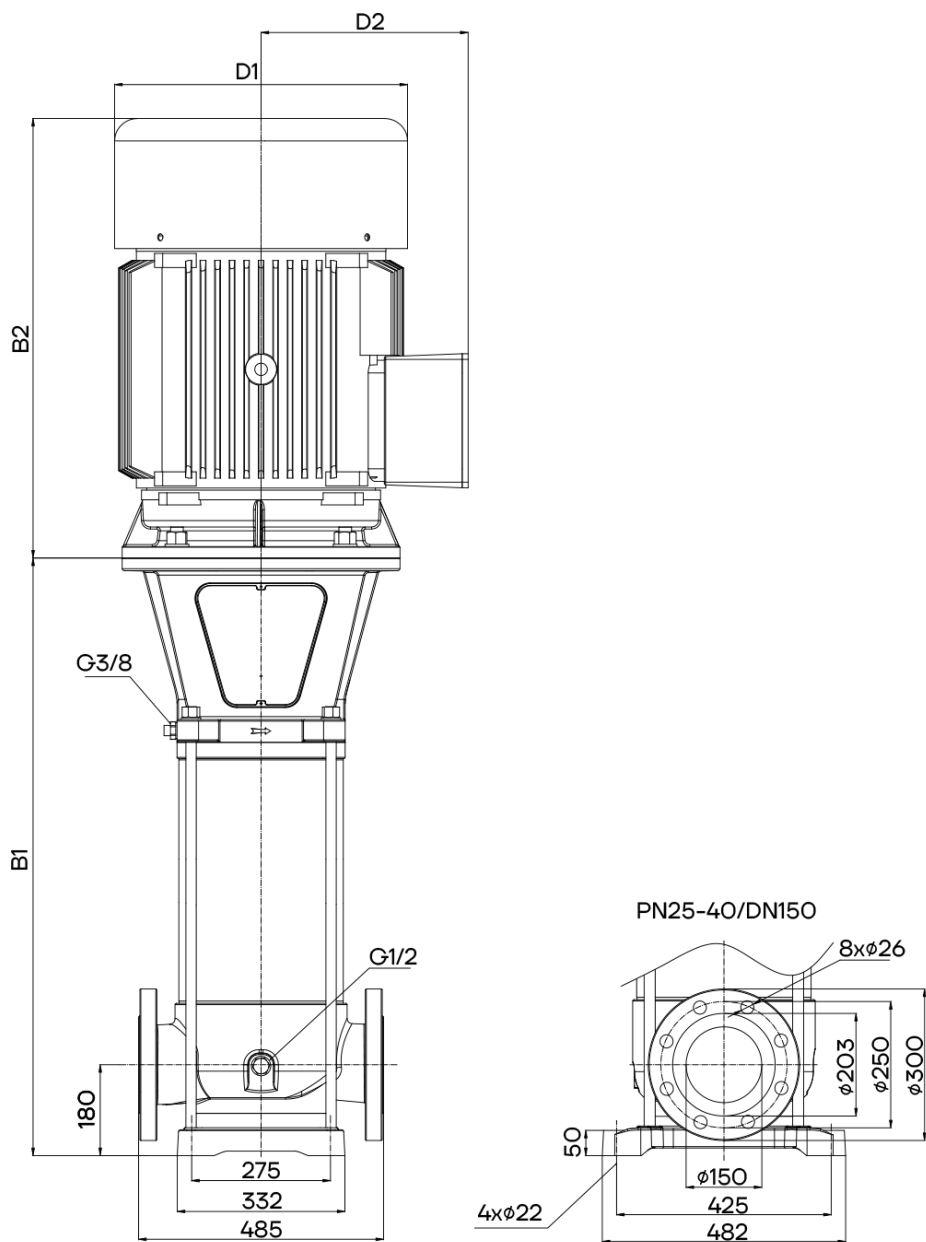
Л Габаритно-присоединительные размеры VMB(F)-H
